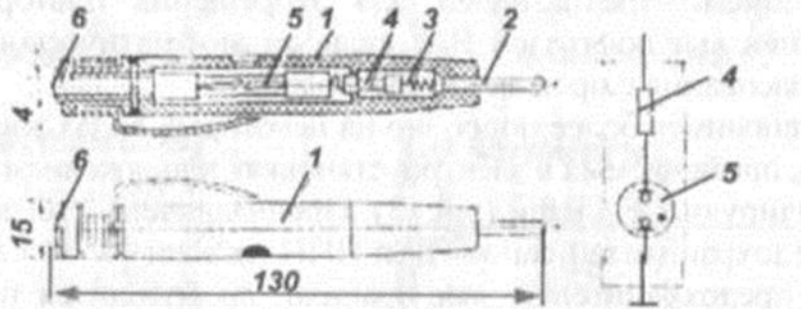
Однополюсный указатель напряжения типа УНН-1: 1-корпус; 2-щуп; 3-пружина; 4- добавочное сопротивление; 5- неоновая лампа; 6-контактная втулка.
